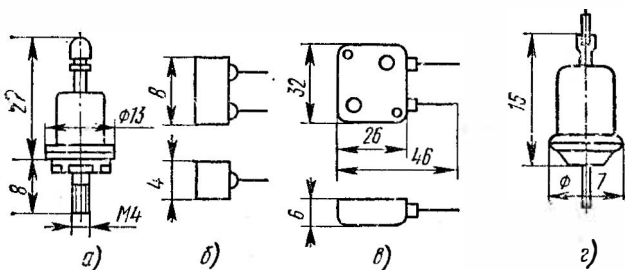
Общий вид и габаритные размеры стабилитронов:
